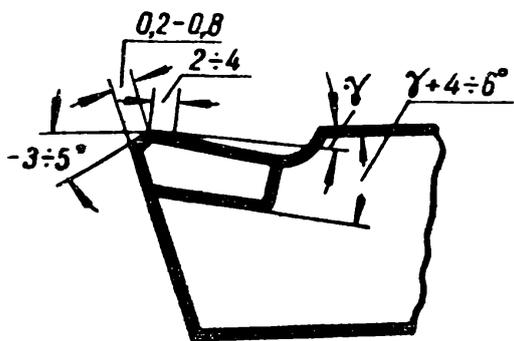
а. Форма заточки резца с пластинкой твердого сплава для обработки чугуна и стали. Заточка плоская с положительным передним углом и отрицательной упрочняющей фаской.
